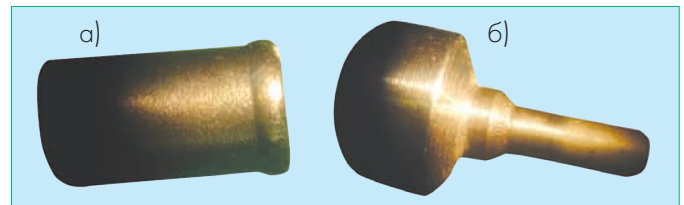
Лазерная микросварка: а) герметизация термокабелей; б) сварка корпуса кабеля со штуцером
